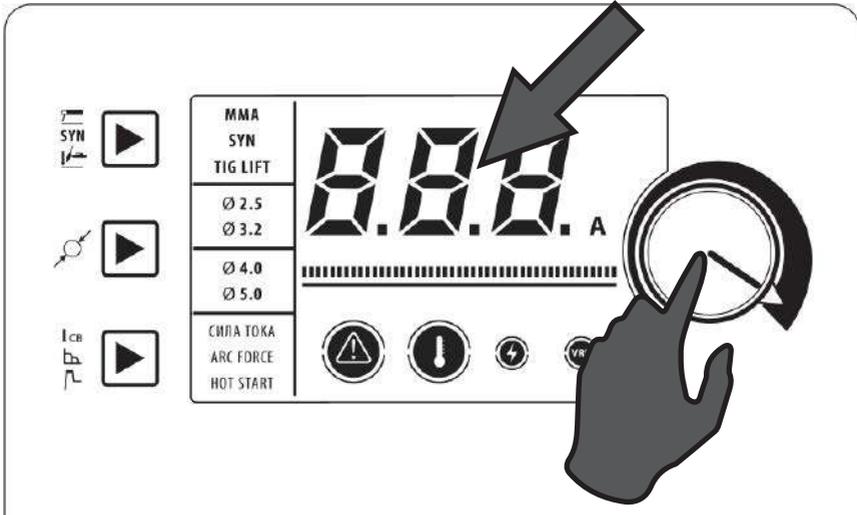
Установка сварочного тока для строжки.
